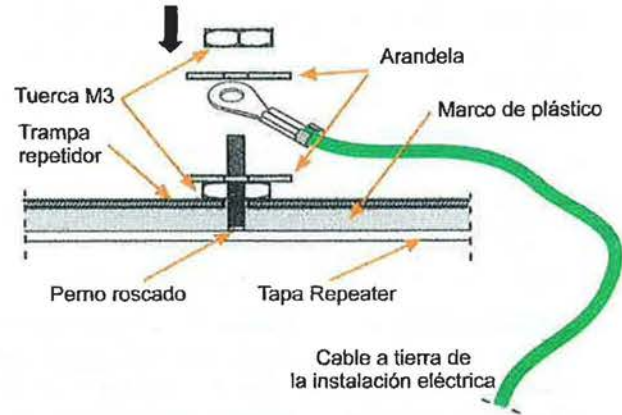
Detalle de piezas y montaje para conectar a tierra una envolvente metálica.
